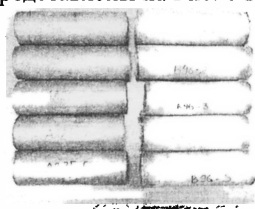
Тиксозаготовки, изготовленные из сплавов АЛ25 и В96Ц3
